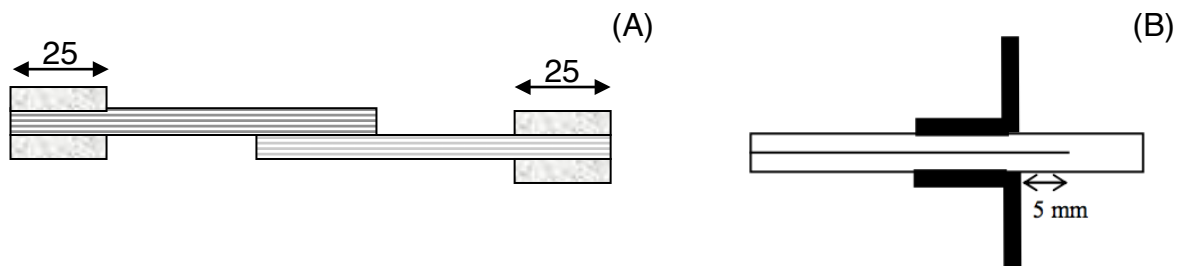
Detalle de la geometría y posición de las chapas en las probetas tipo Z1 (A) y Z2 (B)
